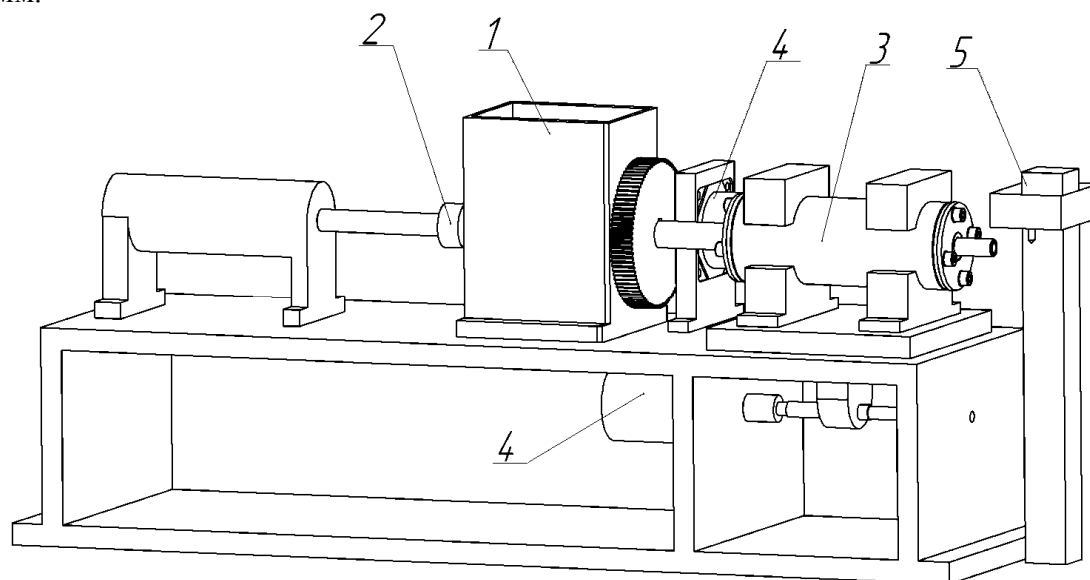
Схема установки для маркировки концевой цилиндрической инструмента
